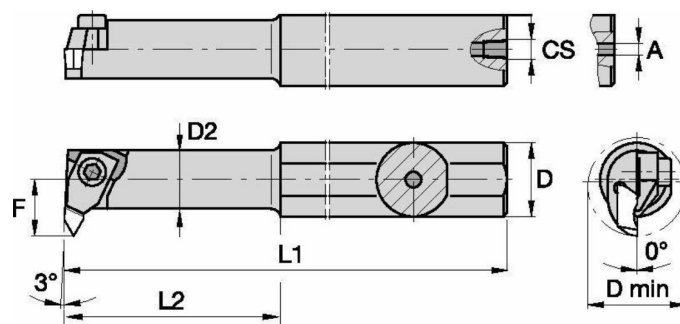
Токарный резьбонарезной резец (для внутренней обработки)
